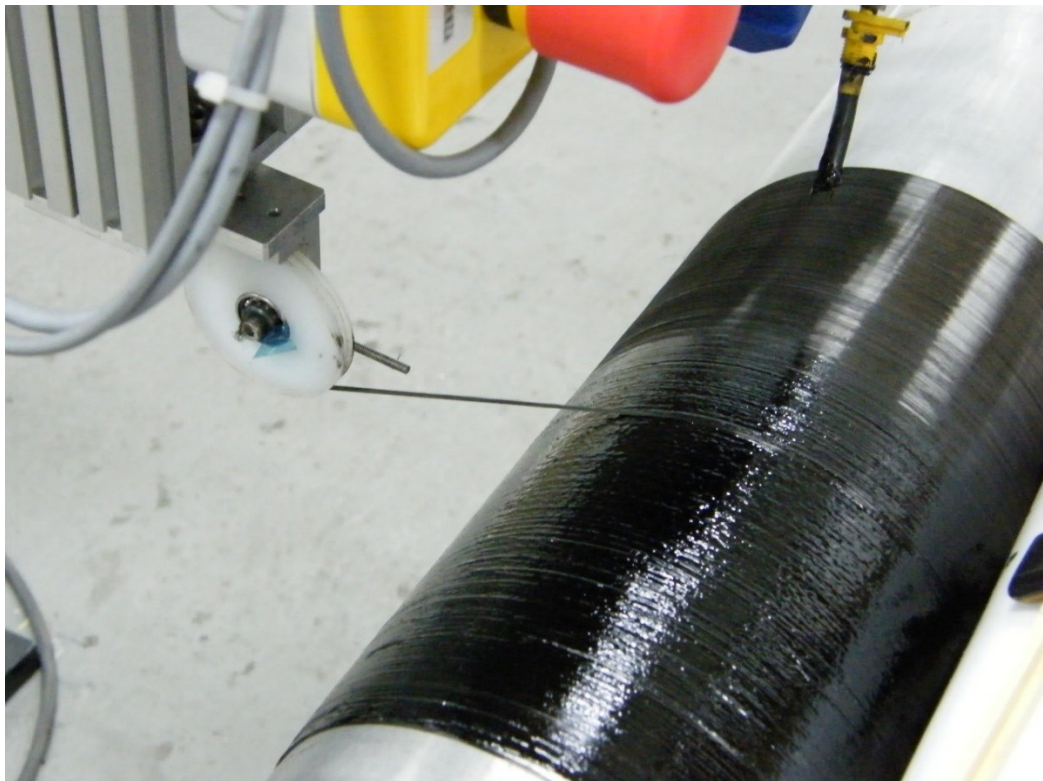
Robotic Wet Winding al CIRA- dettaglio della deposizione wet
